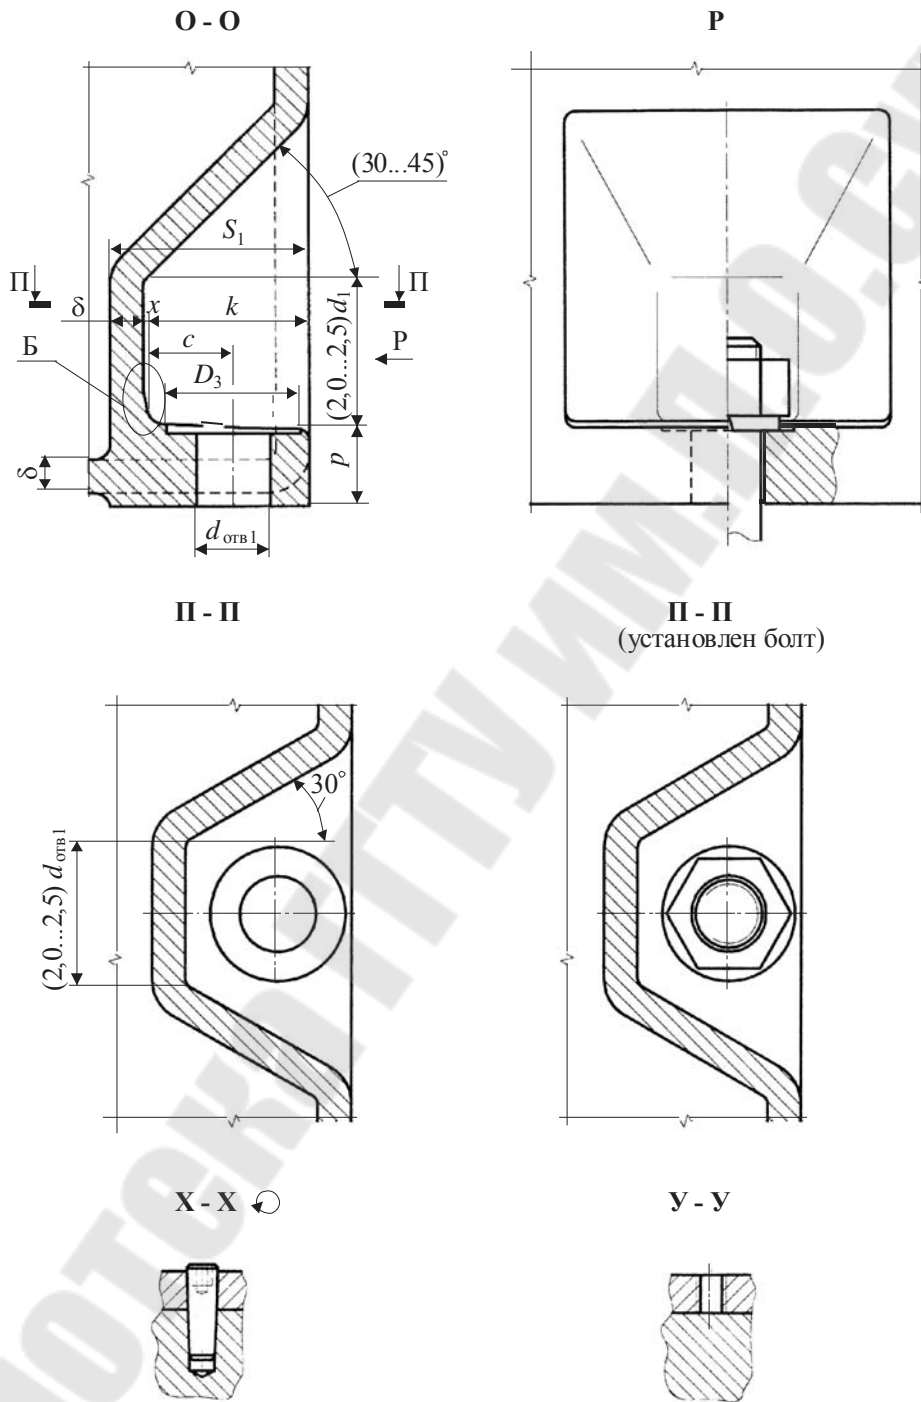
Элементы конструкции корпусных деталей редукторов с внутренним расположением бобышек
